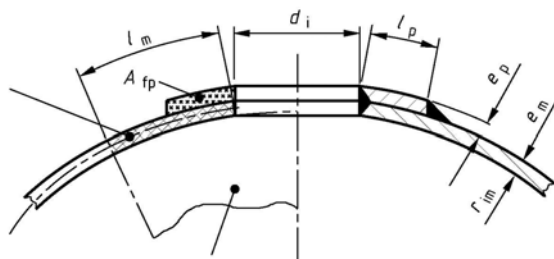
Cálculo de las aberturas — violas cilíndricas con aberturas aisladas (Continuación)
